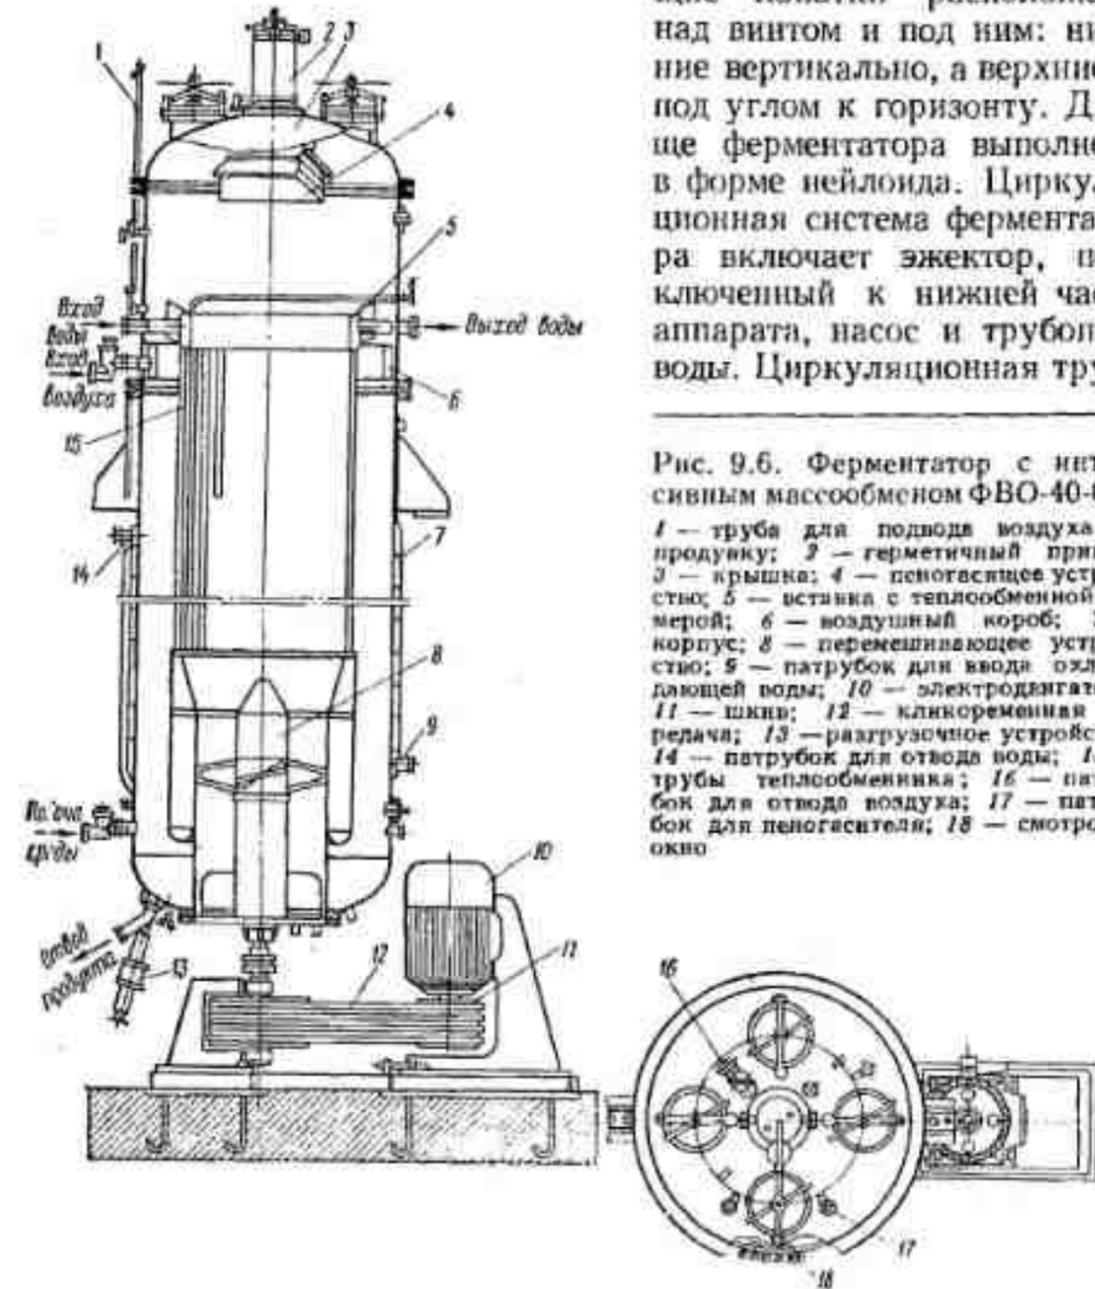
Ферментатор с интенсивным массообменом ФВО-40-0,6: 1 — труба для подвода воздуха на продувку; 2 — герметичный привод; 3 — крышка; 4 — пеногасительное устройство; 5 — установка с теплообменной камерой; 6 — воздушный короб; 7 — корпус; 8 — перемешивающее устройство; 9 — патрубок для ввода охлаждающей воды; 10 — электродвигатель; 11 — шкив; 12 — клиноременная передача; 13 — разгрузочное устройство; 14 — патрубок для отвода воды; 15 — трубы теплообменника; 16 — патрубок для отвода воздуха; 17 — патрубок для пеногасителя; 18 — смотровое окно
